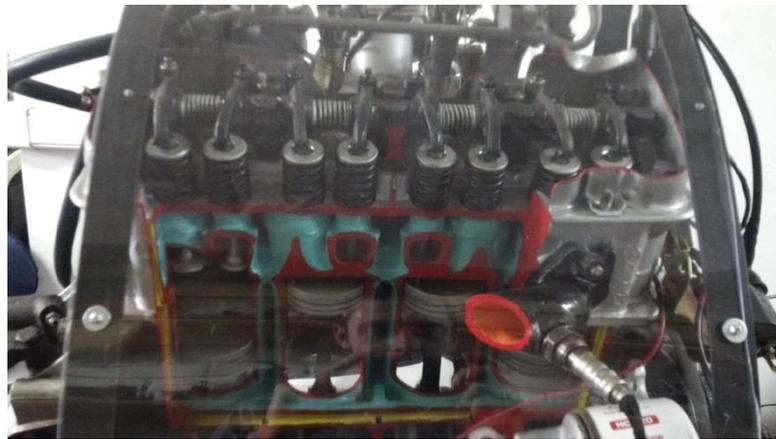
Culata con ensamble completo instalada en el motor de combustión interna.
